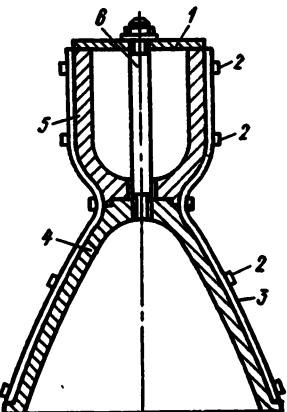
Оправка для сборки КС трубчатой конструкции:
